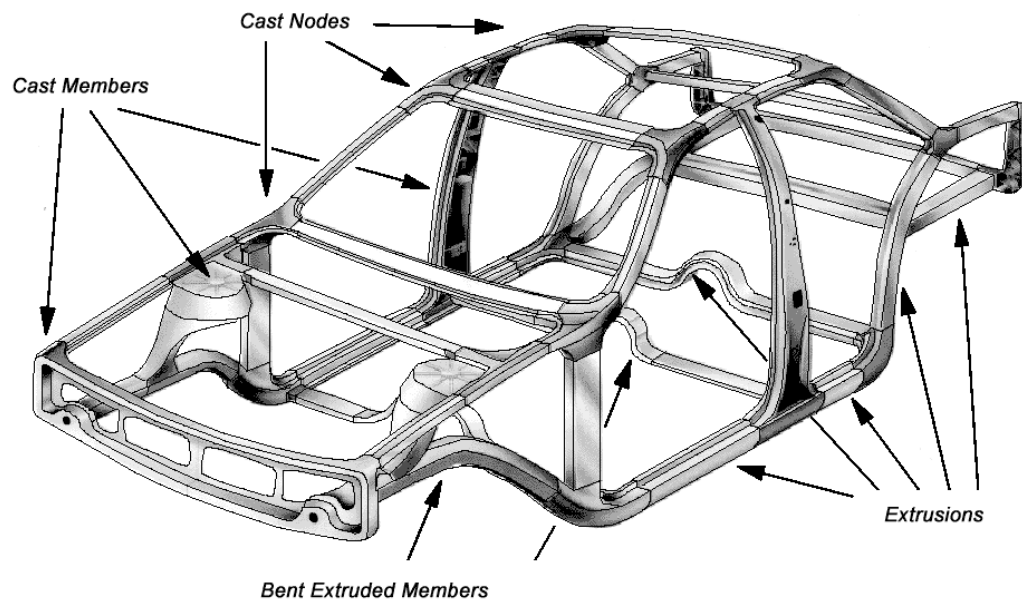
Configurazione generale di telaio Space Frame
